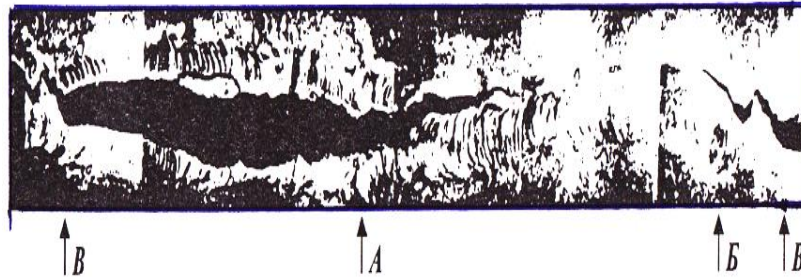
Вид розриву монтажного зварювального з'єднання з боку зовнішньої поверхні: А – початок зварки; Б – кінець зварки; В – зародження тріщини
